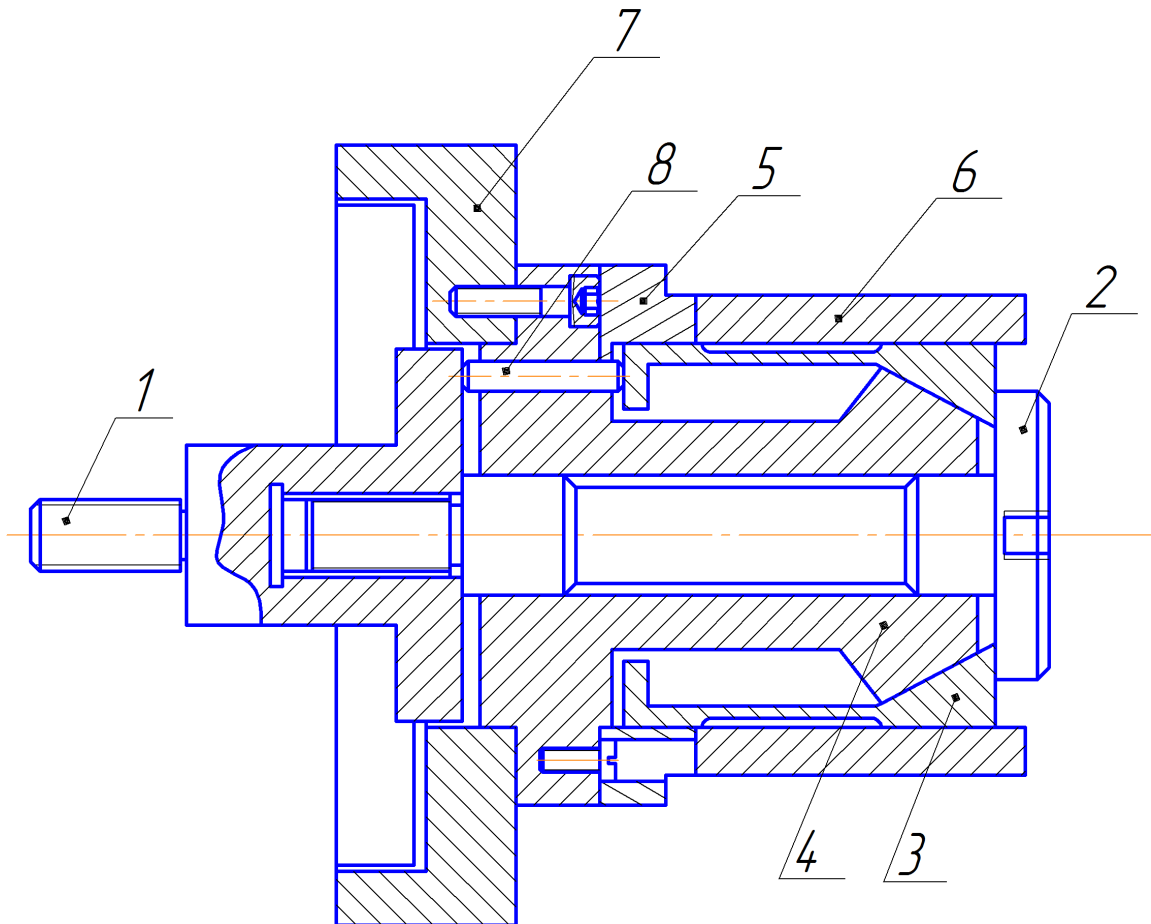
Цанговый механизм зажима заготовки по внутреннему диаметру:
